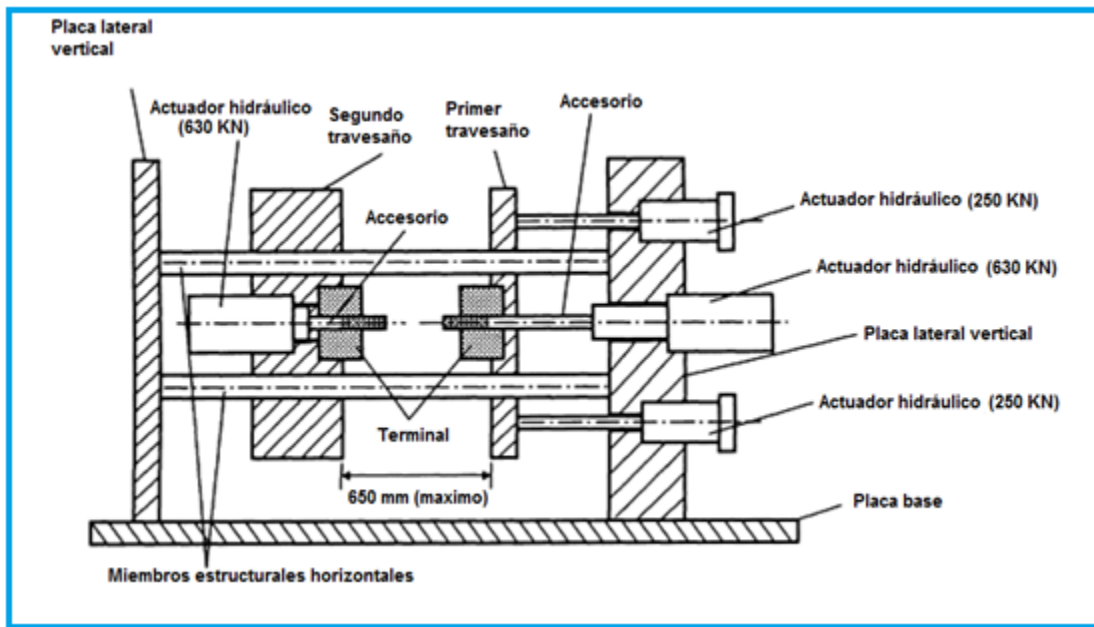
Proceso de soldadura en frío a tope de dos barras, utilizando el método de recalco de múltiple paso.
